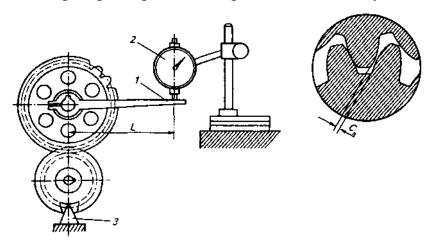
Измерение бокового зазора зацепления: 1 - поводок; 2 - индикатор; 3 - фиксатор
